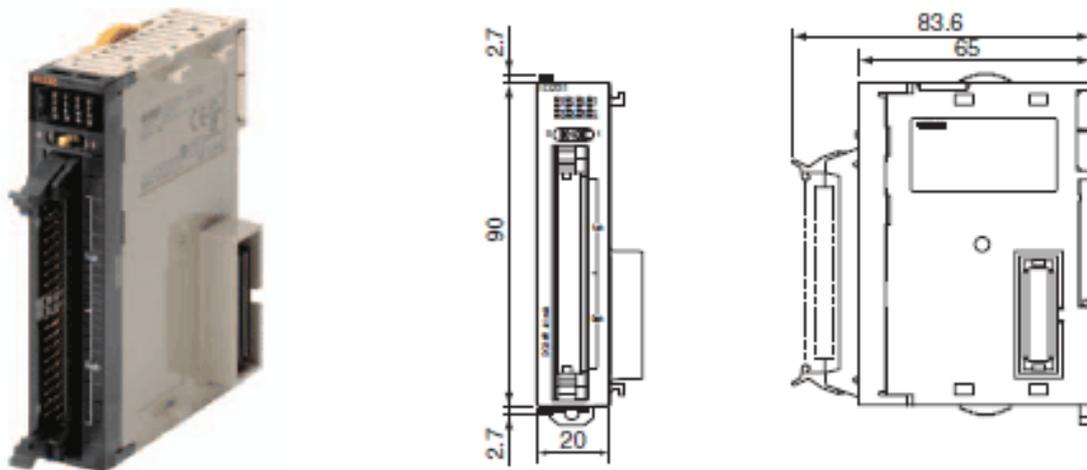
Внешний вид модуля центрального процессора CJ1M-CPU 11
